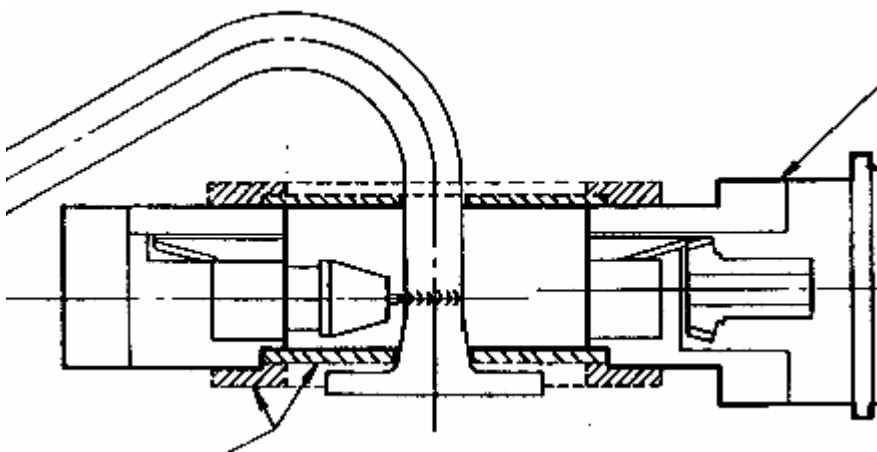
Soldadura bajo atmósfera controlada
